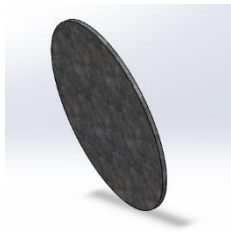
3: TAPA DEL TAMBOR. FUENTE: AUTOR.
